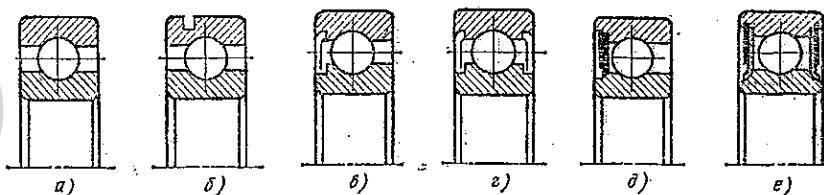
Шарикоподшипники радиальные однорядные типов:
